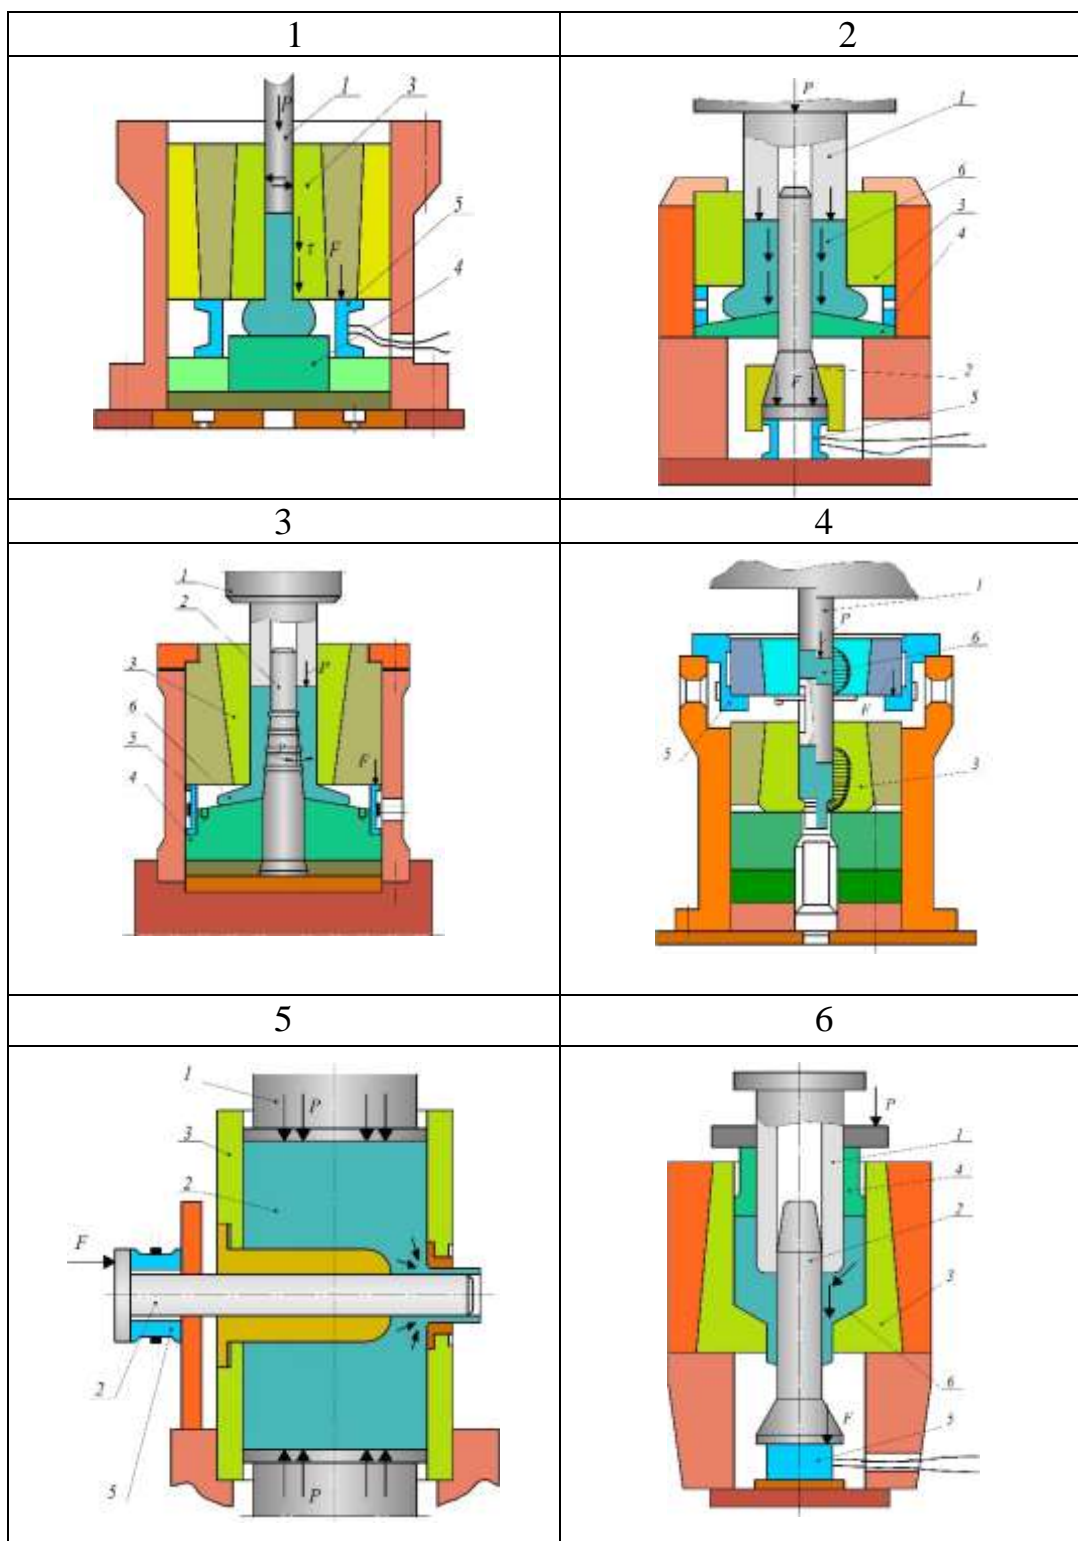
Схеми пристроїв для вимірювання сил контактної тертя:
